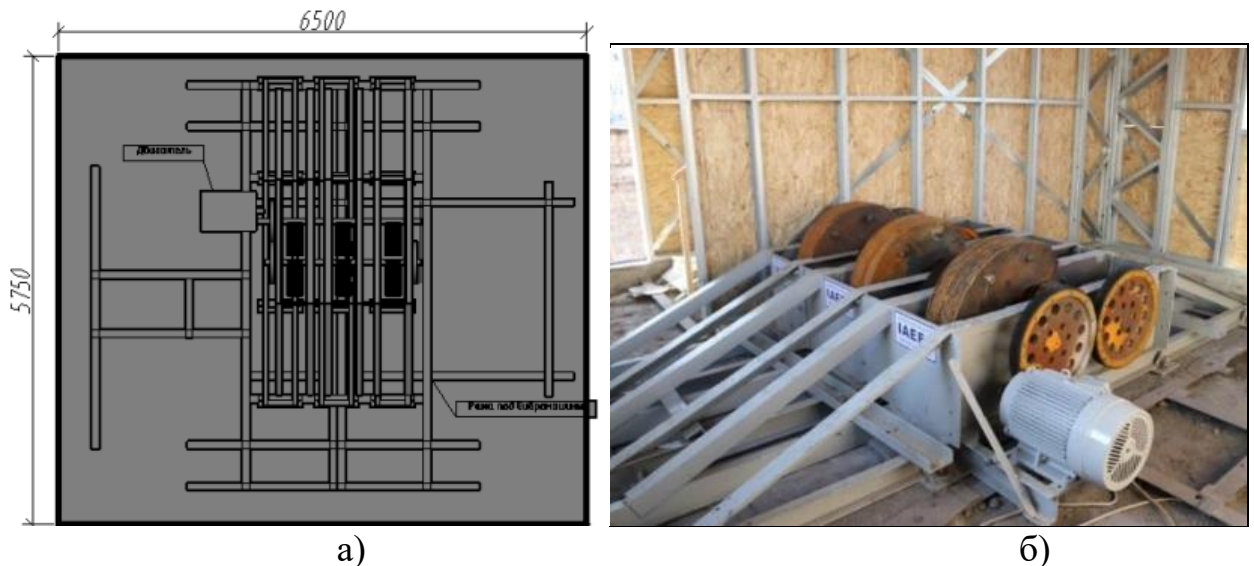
а) схема вибромашины; б) общий вид вибромашины.
